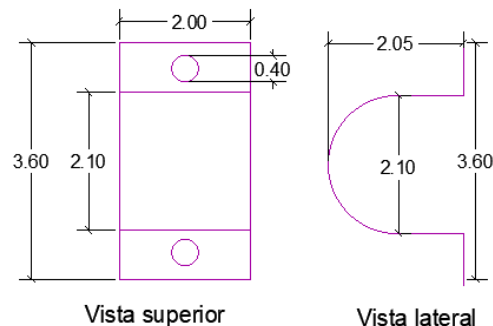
Dimensión en cm y detalle físico de grampa.
